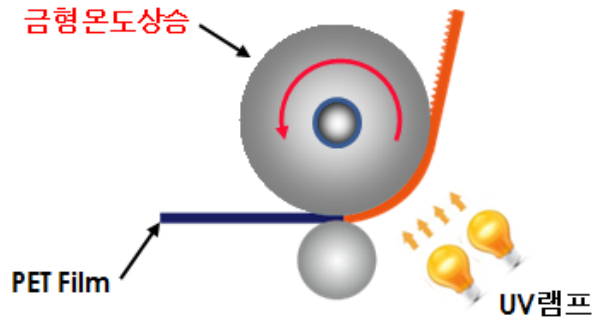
UV 램프에 의한 UV Imprinting 및 금형 온도 상승
